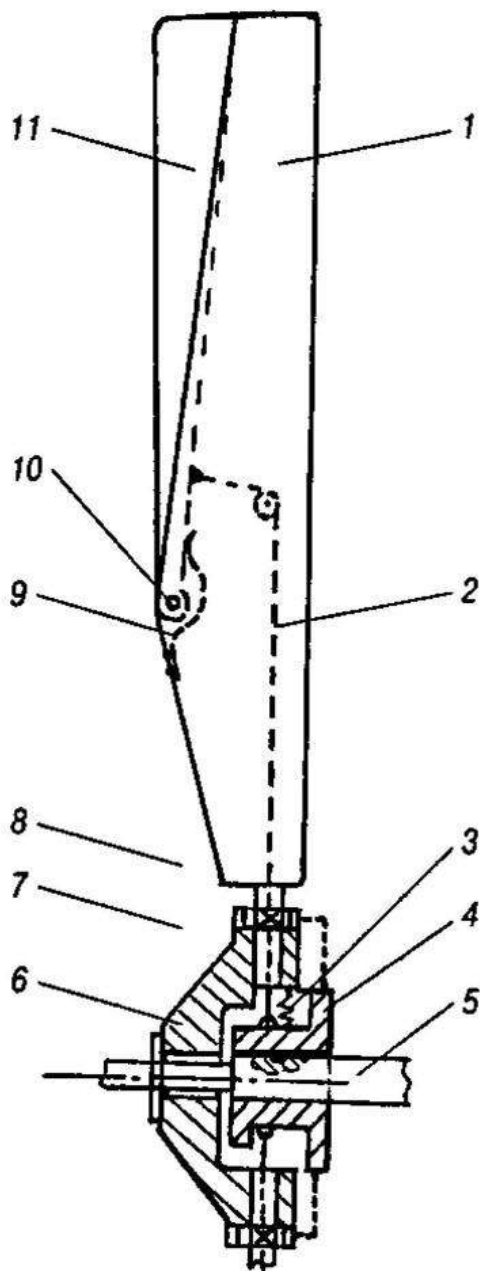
Будова лопаті змінної геометричної форми: 1 — площина лопаті; 2 — тросова тяга; 3 — розпірна пружина; 4 — маточина ротора; 5 — вал; 6 — цапфа лопатей; 7 — механізм повороту лопаті; 8 — вісь лопаті; 9 — пружина закрilка; 10 — вісь висувного закрilка; 11 — висувний закрilок
